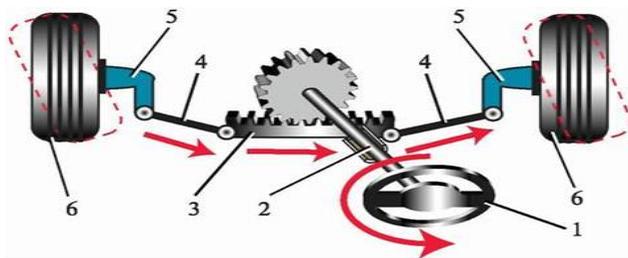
Схема рулевого управления с механизмом типа "шестерня-рейка": 1 – рулевое колесо; 2 – вал с приводной шестерней; 3 – рейка рулевого механизма; 4 – правая и левая рулевые тяги; 5 – поворотные рычаги; 6 – передние колеса автомобиля
